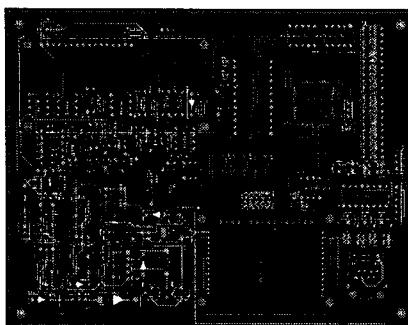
누설전류 센싱 컨트롤러의 PCB Layout
